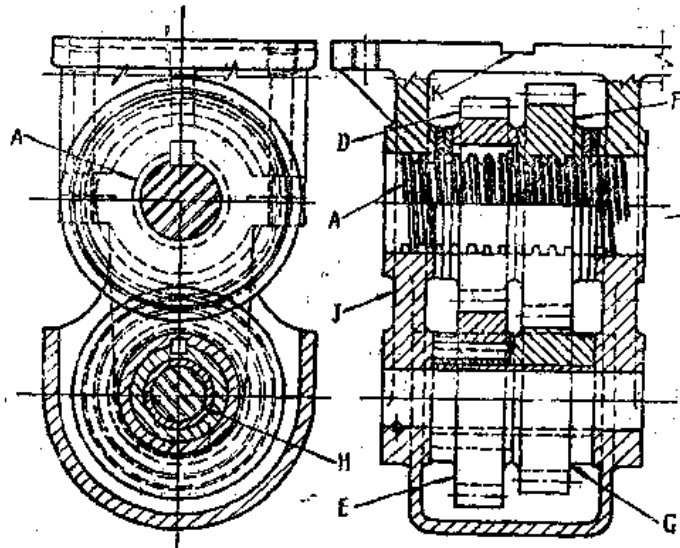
每个连杆支架都有一个由丝杠 A 上的键槽带动的减速齿轮系。齿轮 D 带着键，但仅在丝杠上滑过它通过减速齿轮 E 和 C 带动齿轮 F 驱动螺母而使支架向前移动
